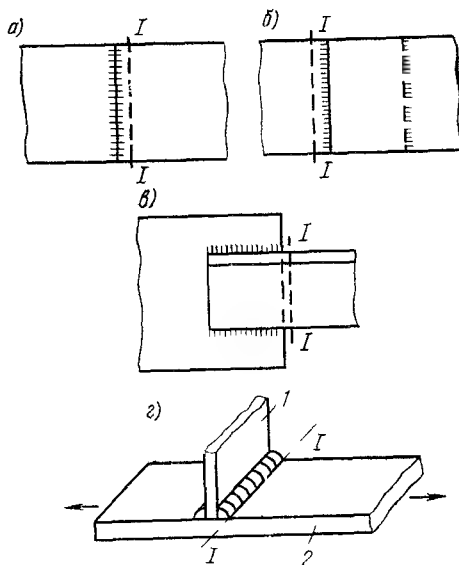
Конструкции и схема сварных соединений
